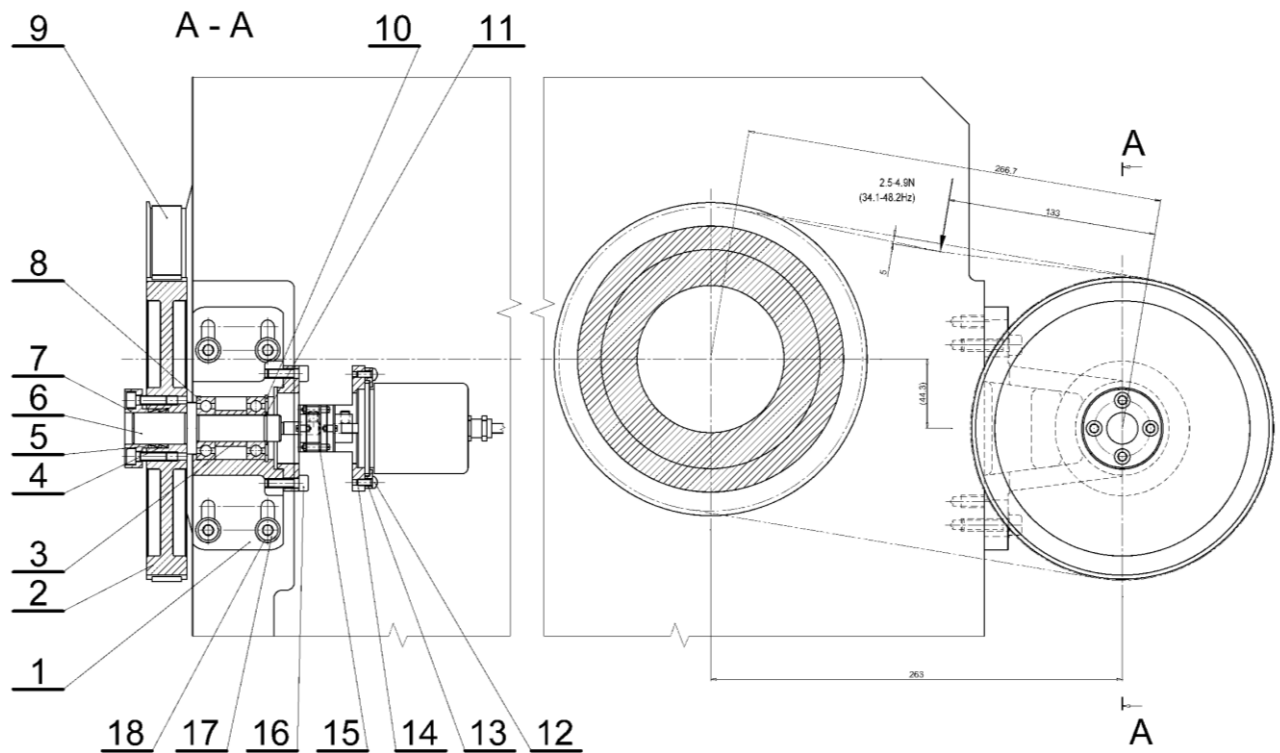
Вимірювальний пристрій для контролю швидкості обертання шпинделя
